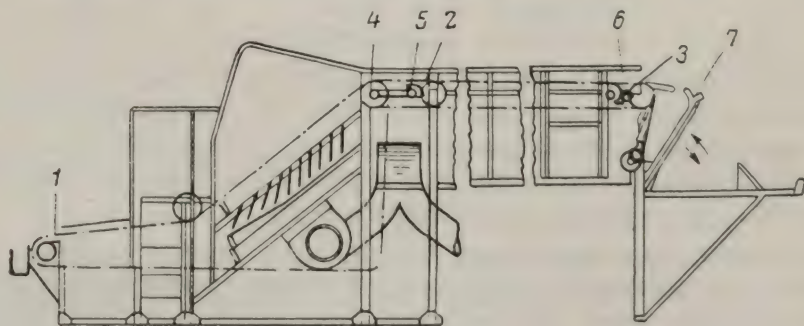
Схема проходного агрегата для окраски и сушки кожи
